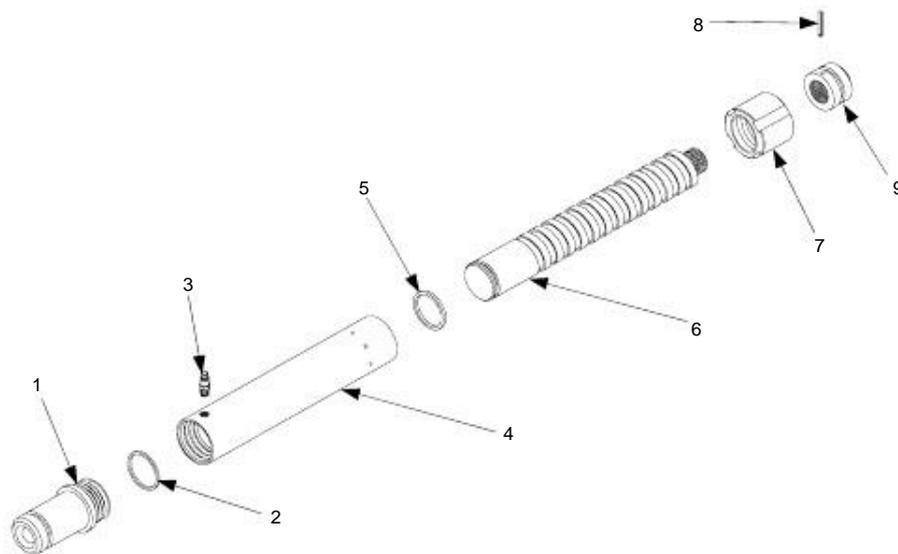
AcmeThread-Stütze, Explosionszeichnung
